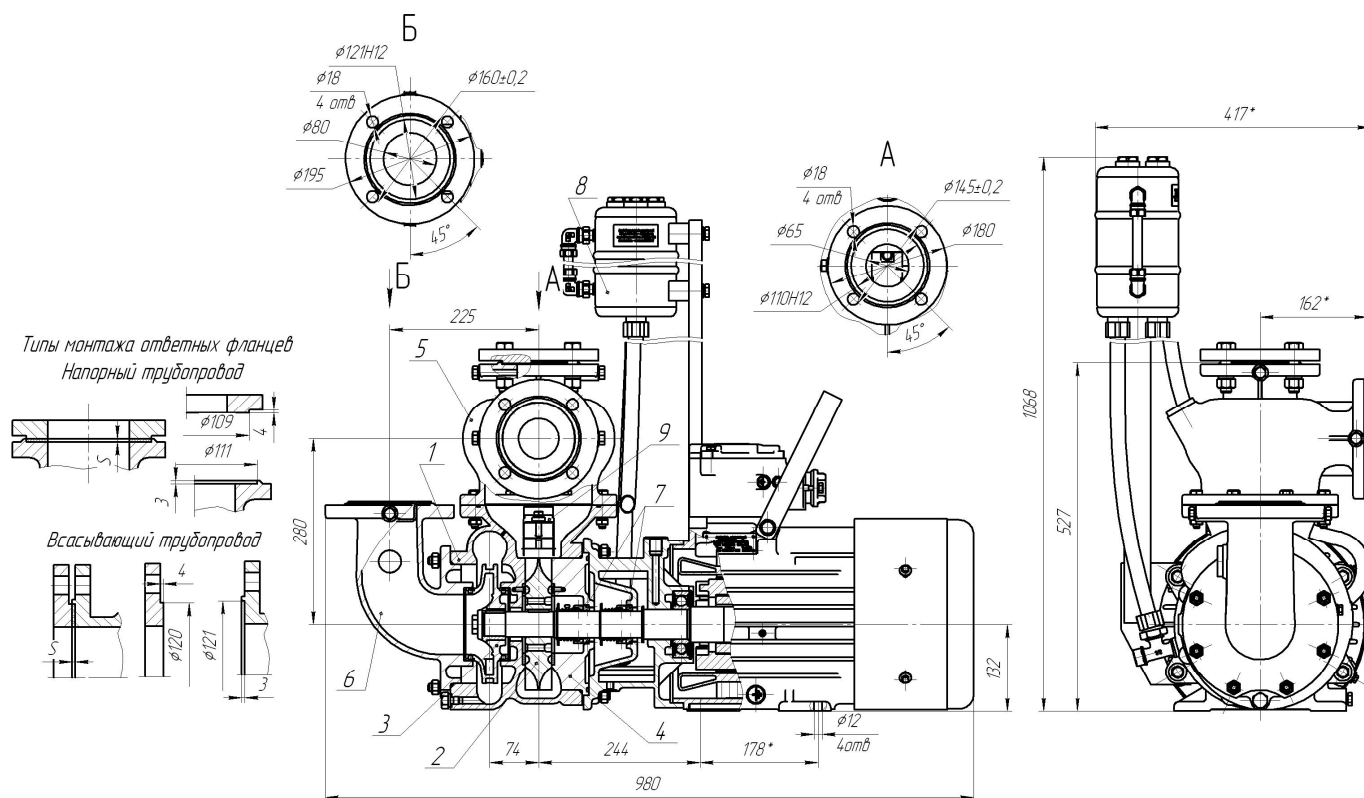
Габаритные и присоединительные размеры КМВГ 40-25-150Е для установки в УИЖГЭ-20
